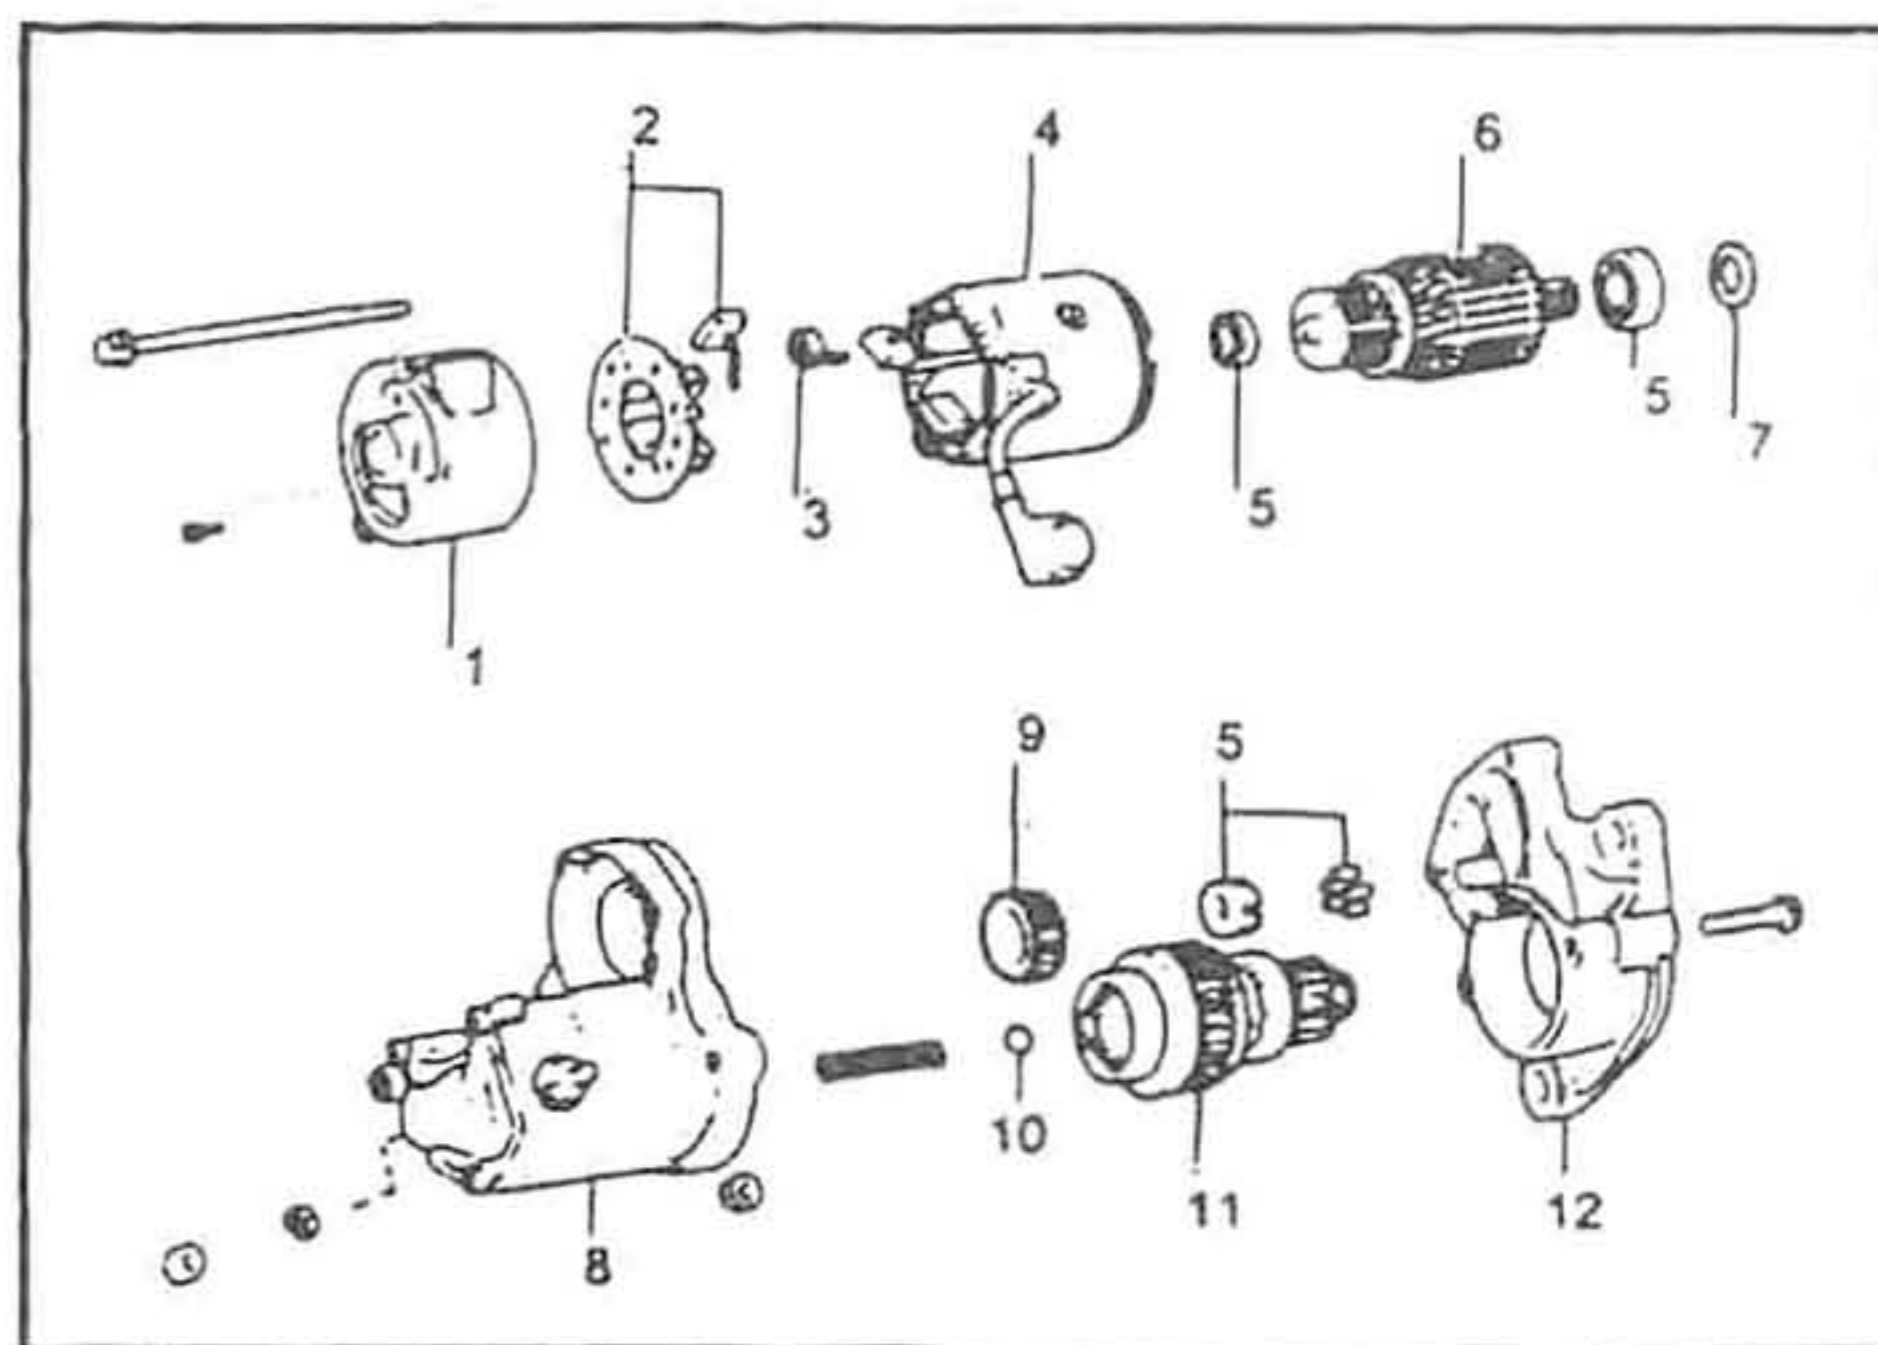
1. Крышка. 2. Щеткодержатель. 3. Пружина щетки. 4. Корпус. 5. Подшипник. 6. Ротор. 7. Войлочное уплотнение. 8. Корпус магнитной муфты. 9. Промежуточная шестерня. 10. Стальной шарик. 11. Муфта. 12. Корпус.
